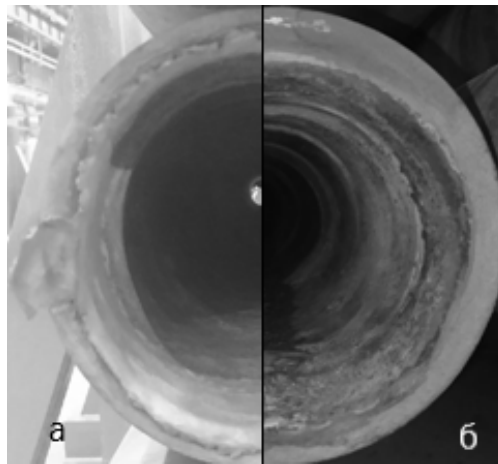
Задний торец труб без зацентровки (а) и с зацентровкой (б) заднего торца заготовки
